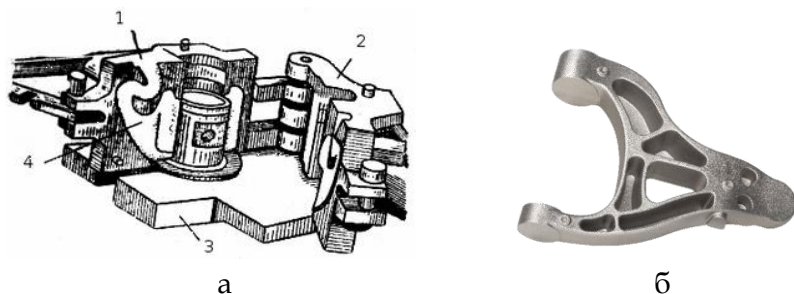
Разъёмный кокиль для изготовления алюминиевого поршня (а) и отливка рычага (б)
